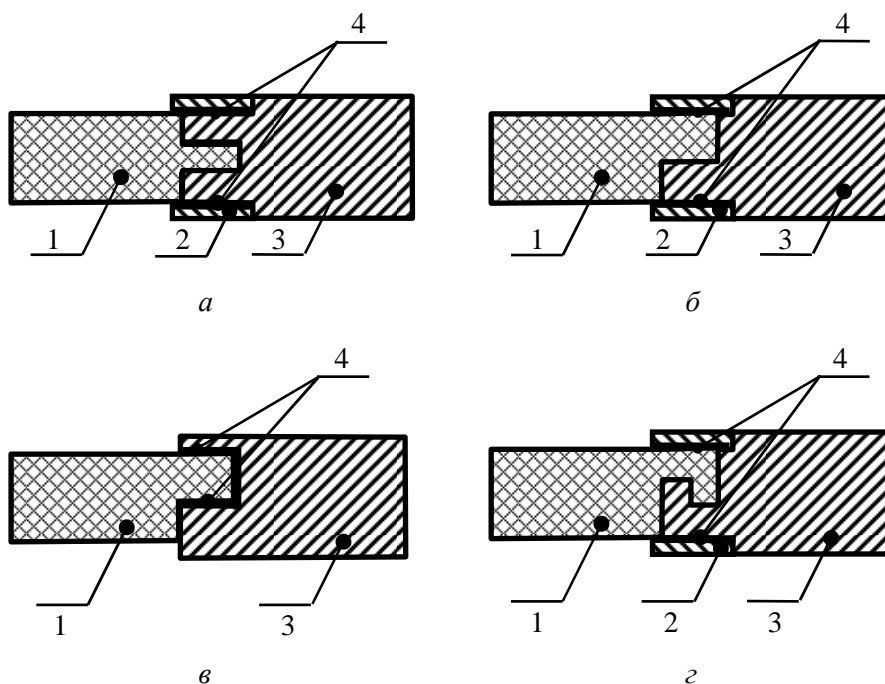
Различные конструкции механического зацепления металлической и керамической деталей: *a* — прямоугольный шип-паз; *б* — сочленение обычных полукруглых торцов; *в* — круглый шип-отверстие; *г* — сочленение фигурных полукруглых торцов; 1 — керамическая деталь; 2 — металлическая втулка; 3 — металлическая деталь; 4 — припой
